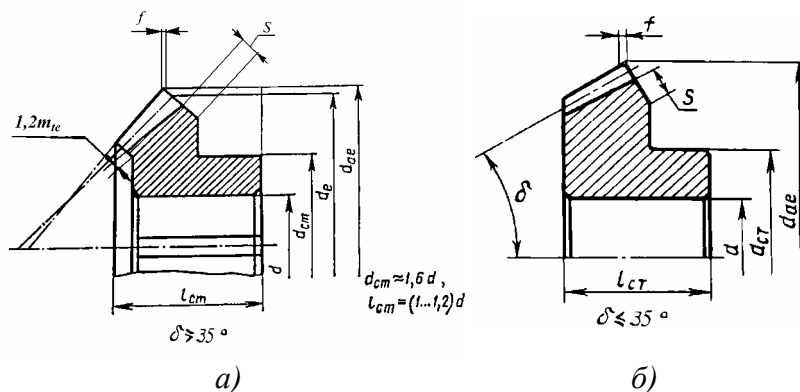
Конструкции конических зубчатых колес малых диаметров
